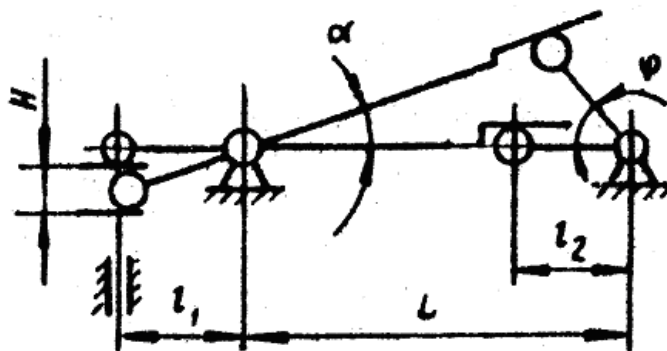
Двухрычажный механизм с ведущей внутренней кулисой
